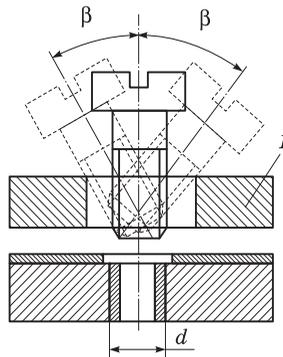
Свинчивание резьбы пары с использованием направляющей втулки
